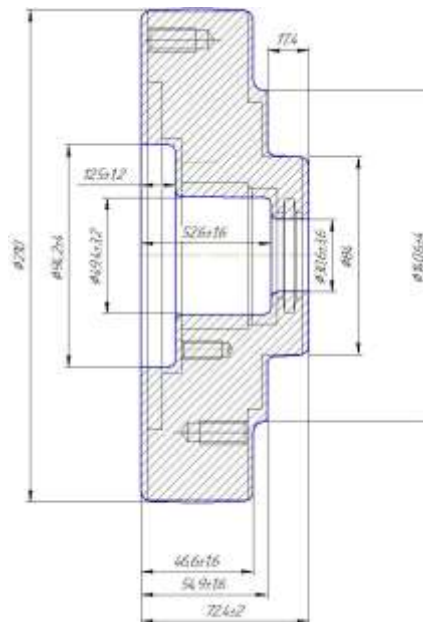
Ескіз заготовки при виготовленні її литтям в піщано-глинисті форми
